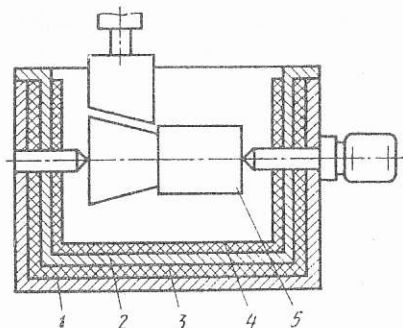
Приспособление для обработки раскатного вала пластинчатым ЭИ с нагревом рабочей жидкости
